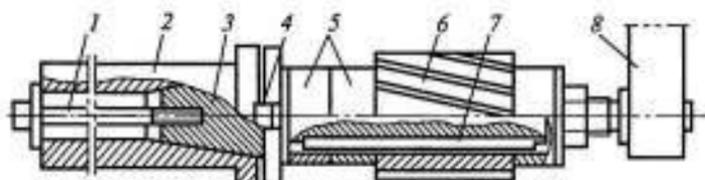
Установка цилиндрической фрезы на длинной оправке:
